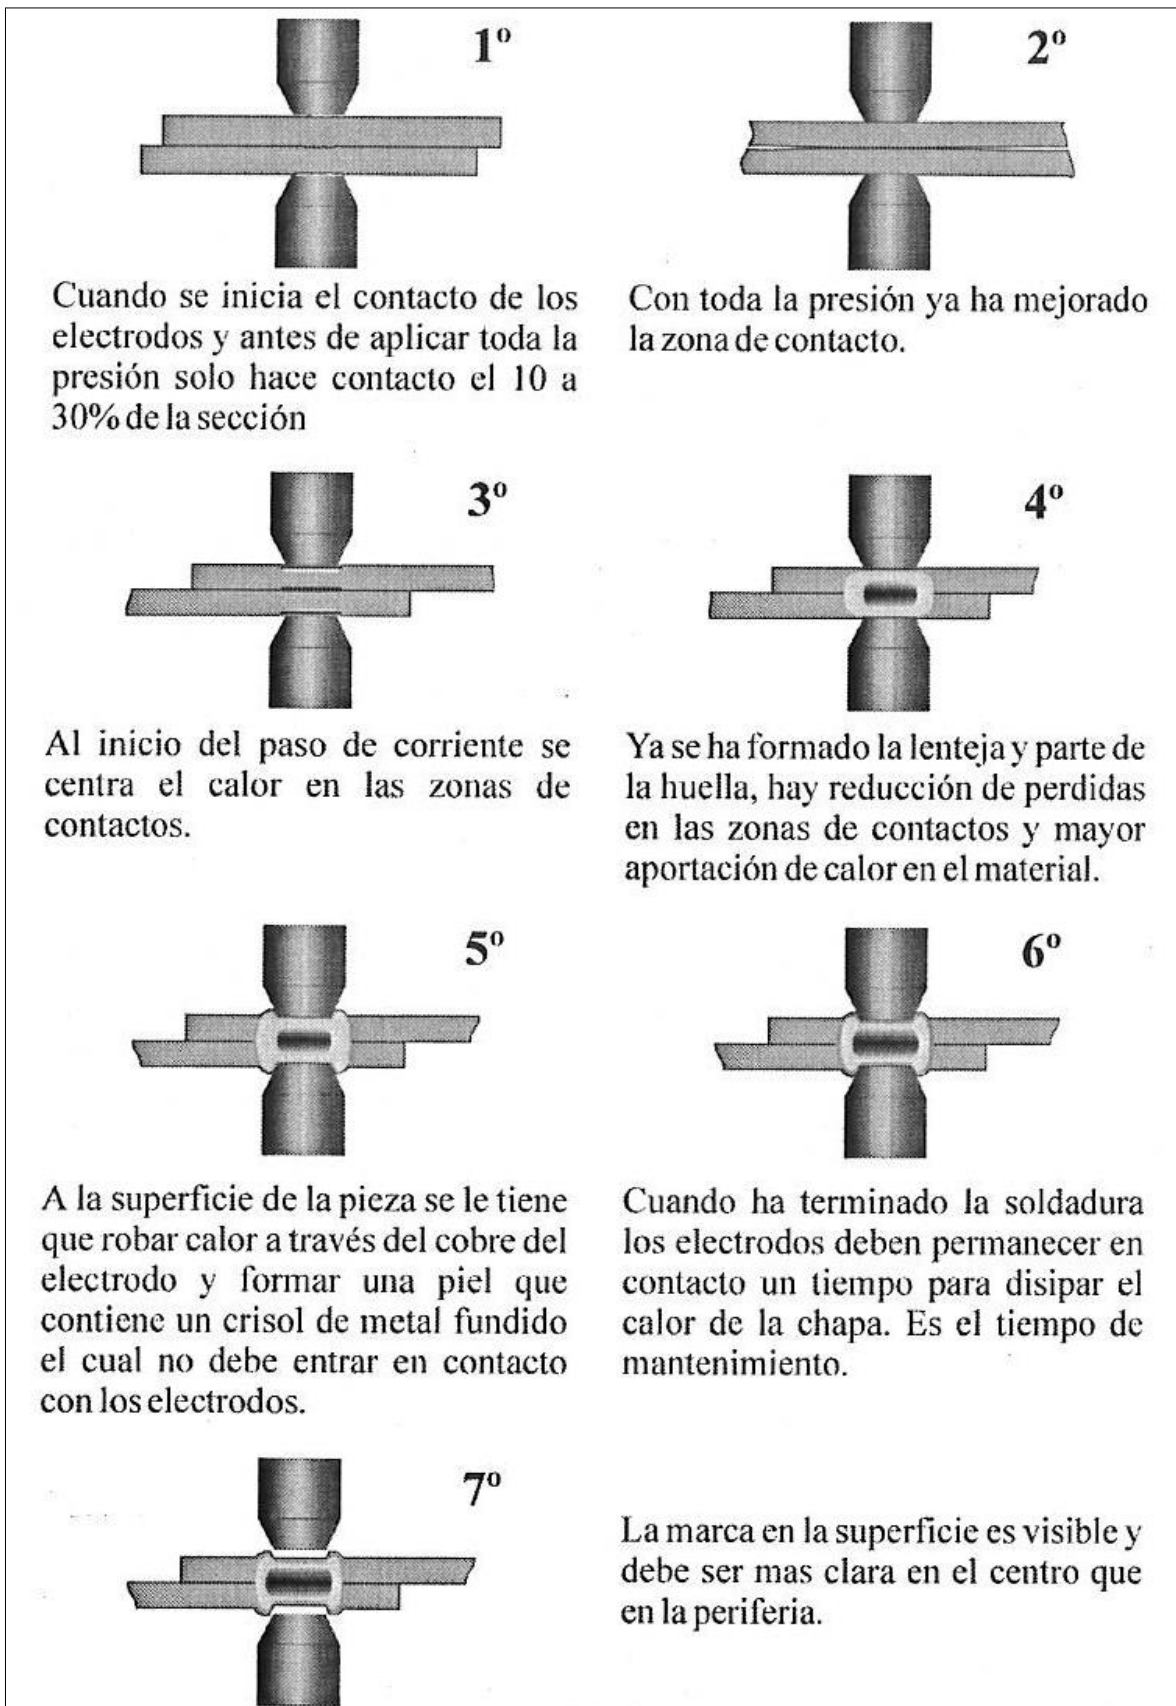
Detalle secuencial de la manera en que se forma un punto de soldadura.
